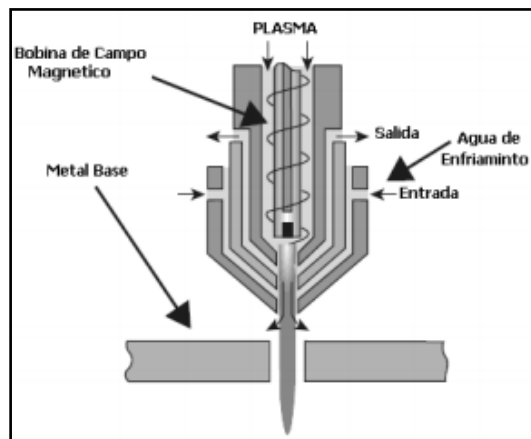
Esquema ilustrativo de boquilla para corte plasma de alta tolerancia [16].
